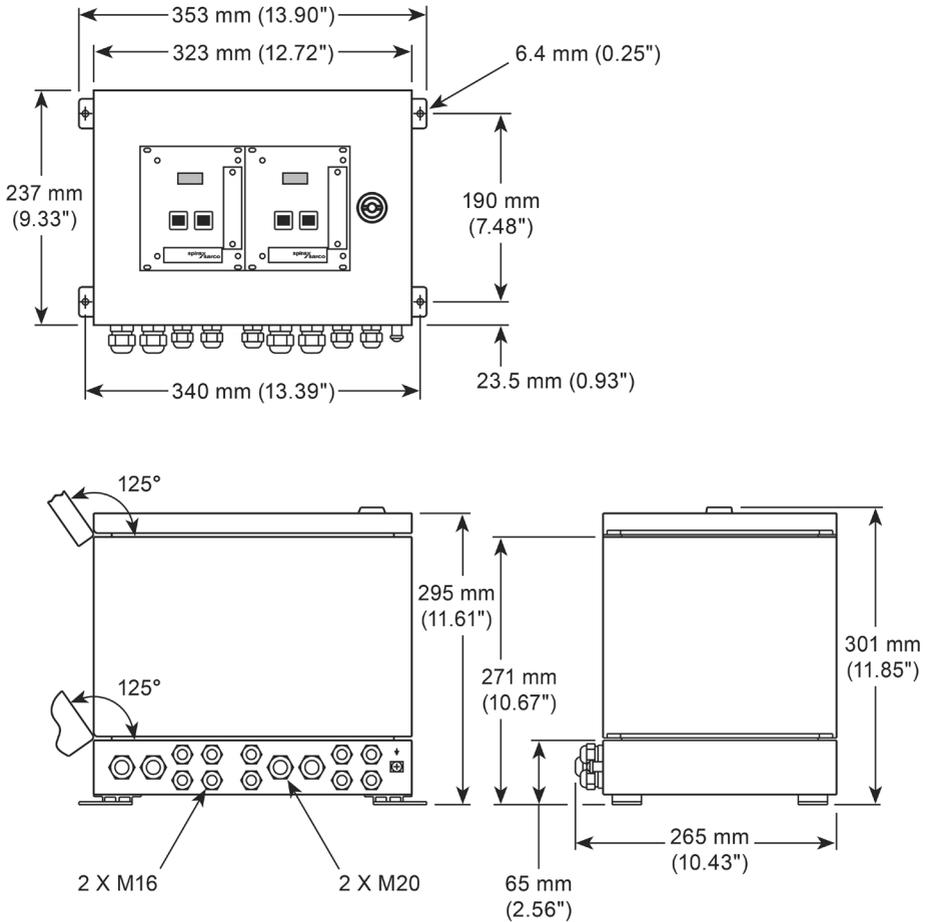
Dimensioni con custodia per montaggio a parete B19-42
